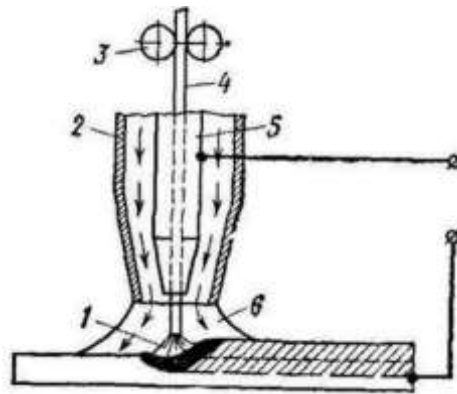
Схематичне зображення зварювання в середовищі захисних газів: 1- зварювальна дуга; 2- сопло; 3- подавальні ролики; 4- електродний дріт; 5 - струмопідводний мундштук; 6 - газовий захист [2]
